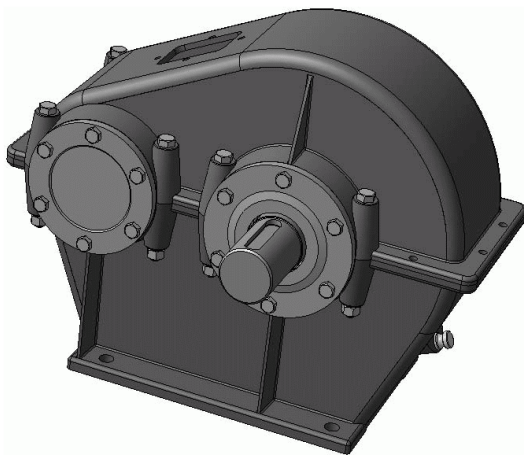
а. Литий корпус одноступінчастого циліндричного редуктора традиційного типу
